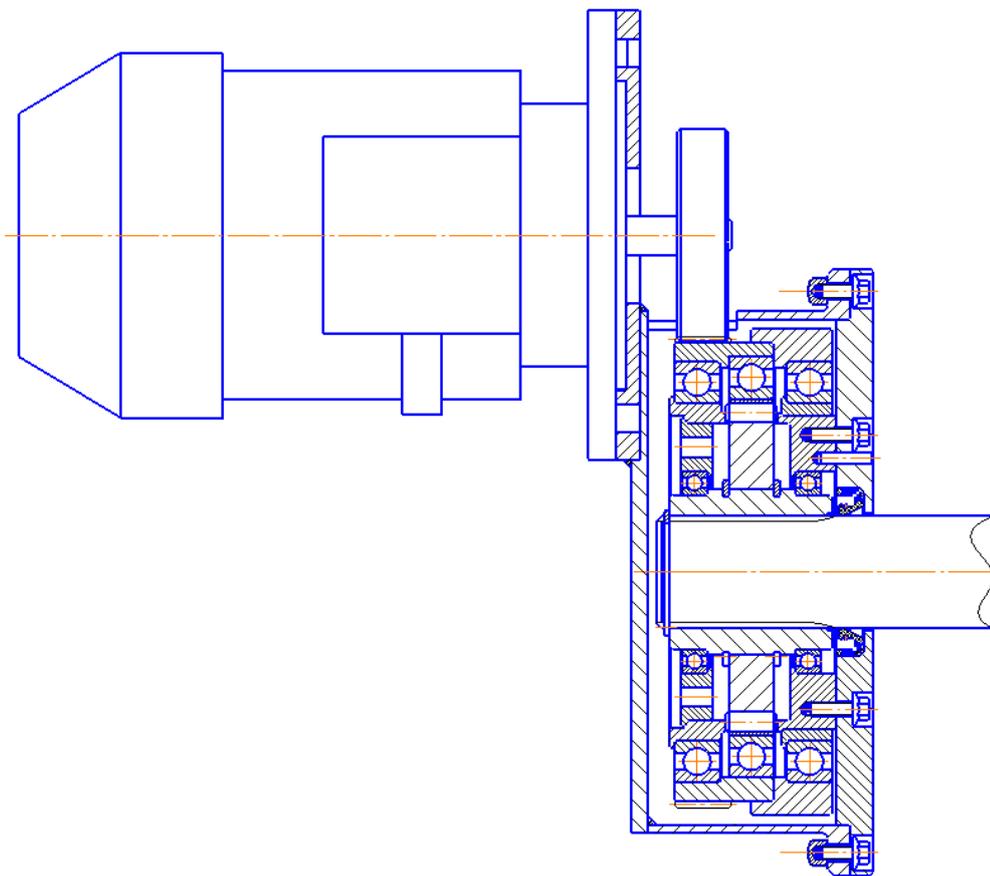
Схема привода волнового редуктора с внешним зубчатым зацеплением.
